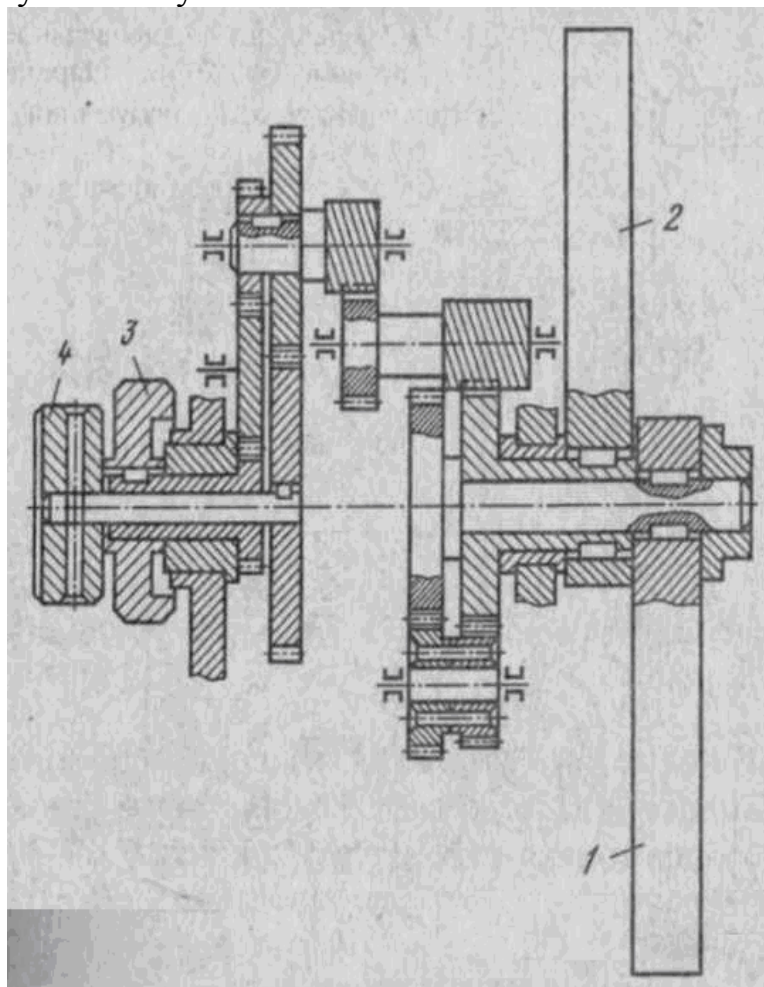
Кинематическая схема механизма для балансировки шлифовальных кругов: 1, 2 – грузы, 3, 4 – рукоятки.
